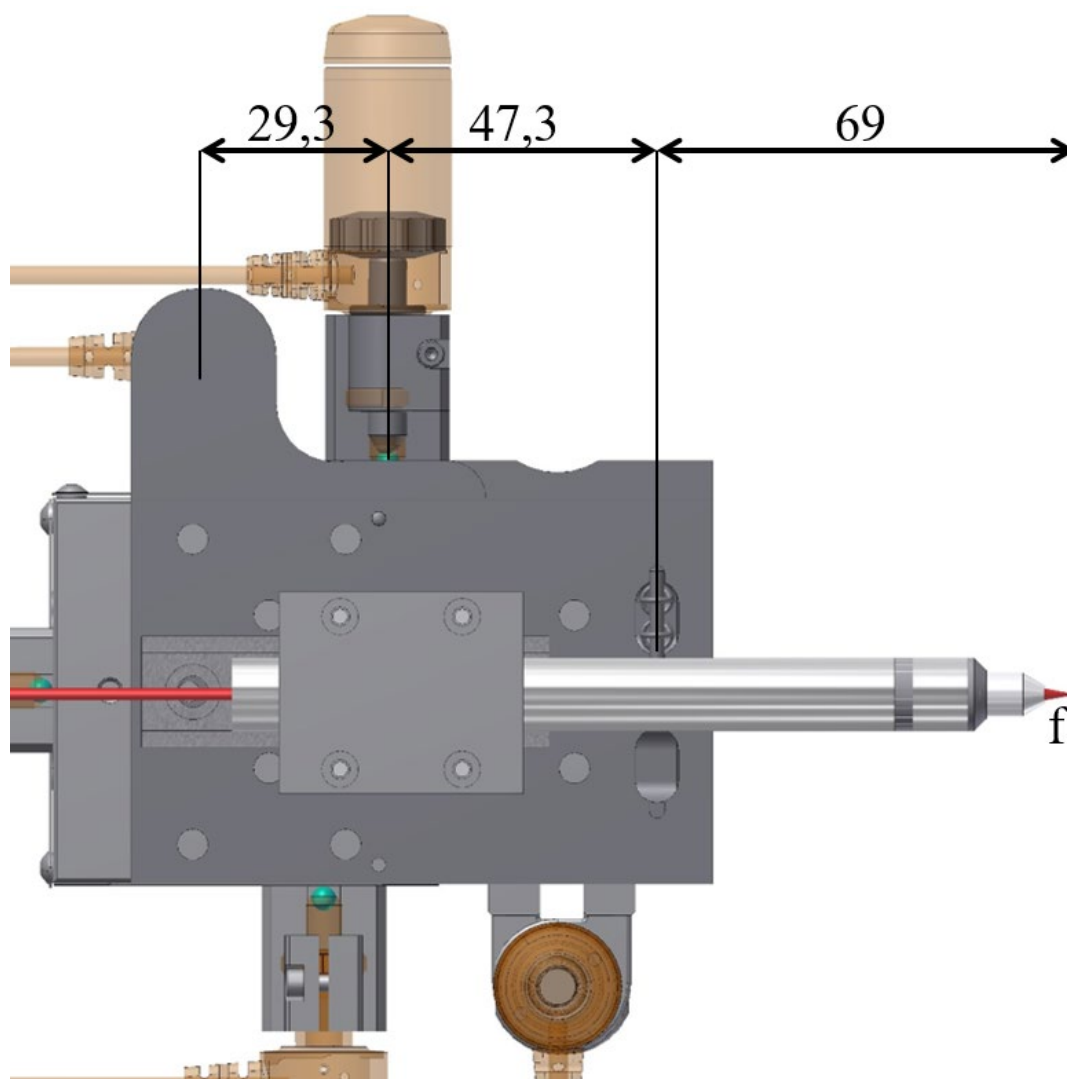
Схема расположения элементов сборки линзы на столике с указанными линейными размерами
